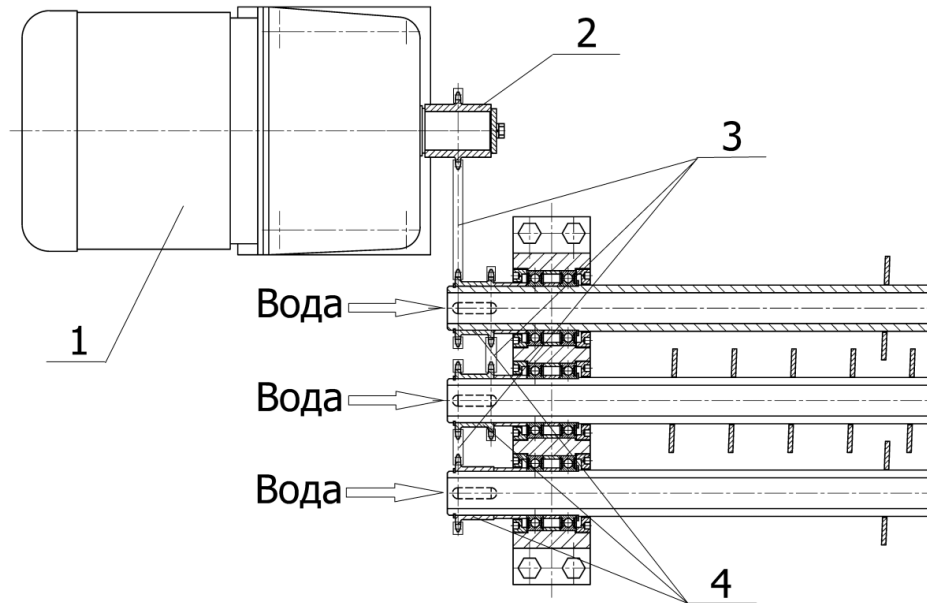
Главный привод шнекового транспортера: 1 – мотор-редуктор; 2 – звездочка ведущая; 3 – цепь; 4 – звездочки ведомые
